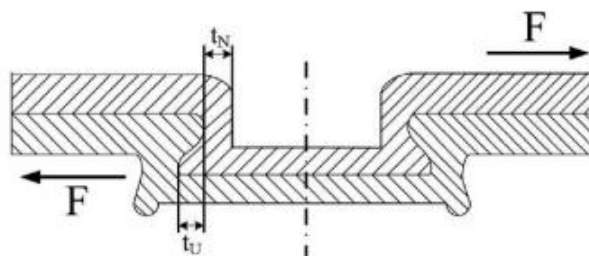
Parâmetros da UCCF em vista de corte, (LEI e TONGXIN, 2019)
